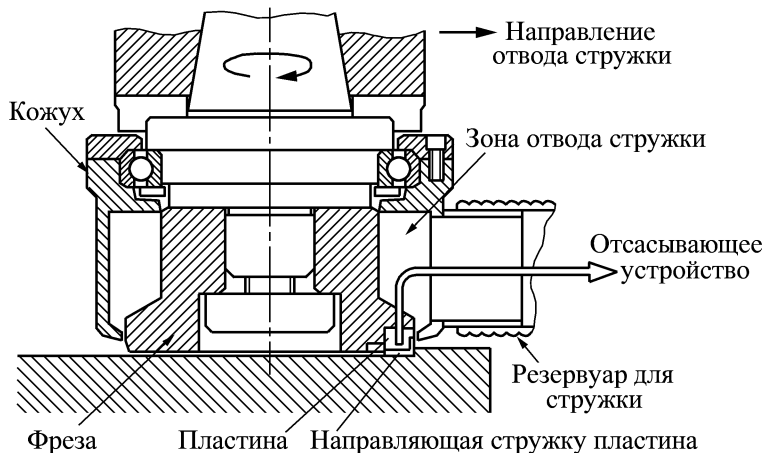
Устройство автоматического отвода стружки при фрезеровании
